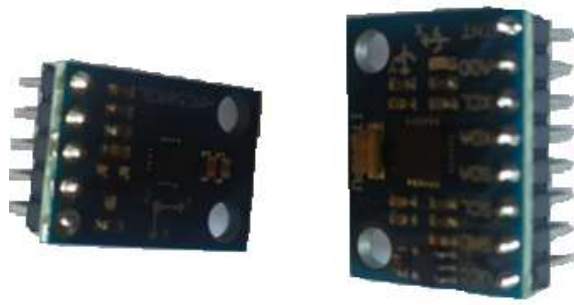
Soldagem conector Through Hole 5 e 8 posições.
